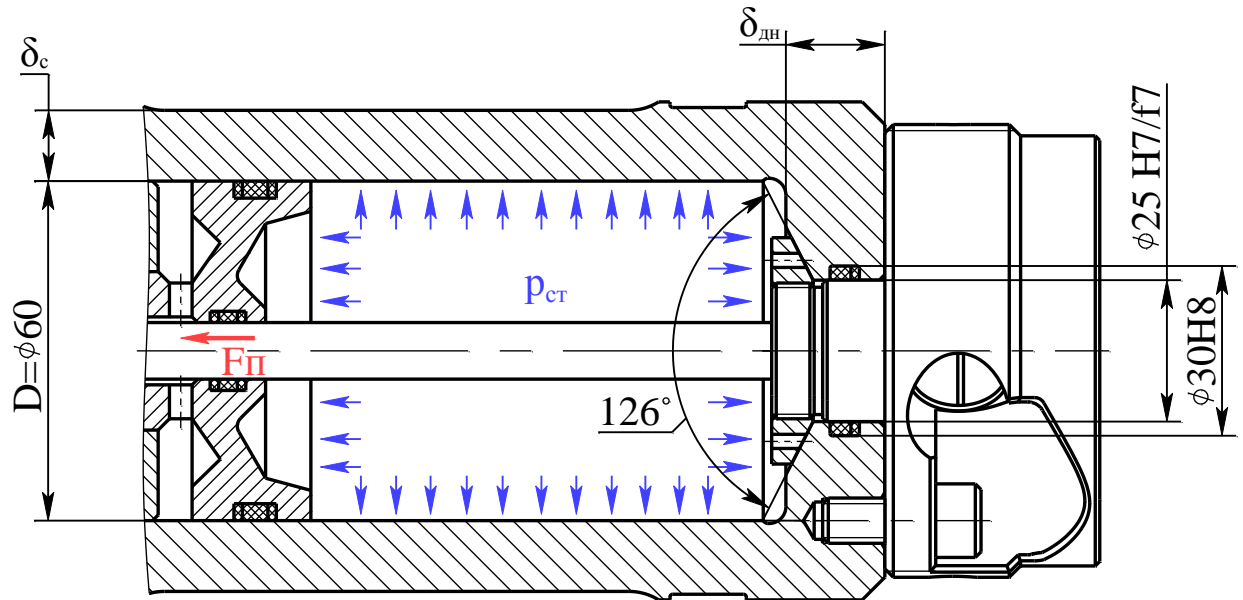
Эскиз для расчета корпуса гидроцилиндра
